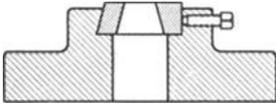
Befestigung der Schnittplatte durch einfache Schräge und Druckschraube.
